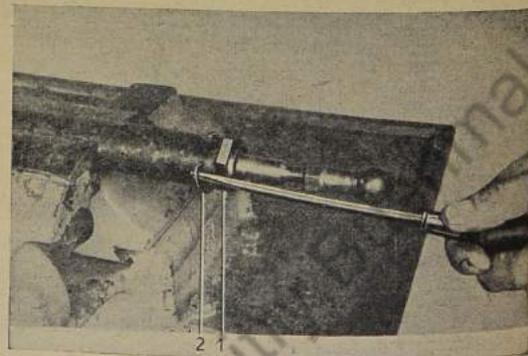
Verschlusschraube in Kuppelstange entsichern und herausschrauben
